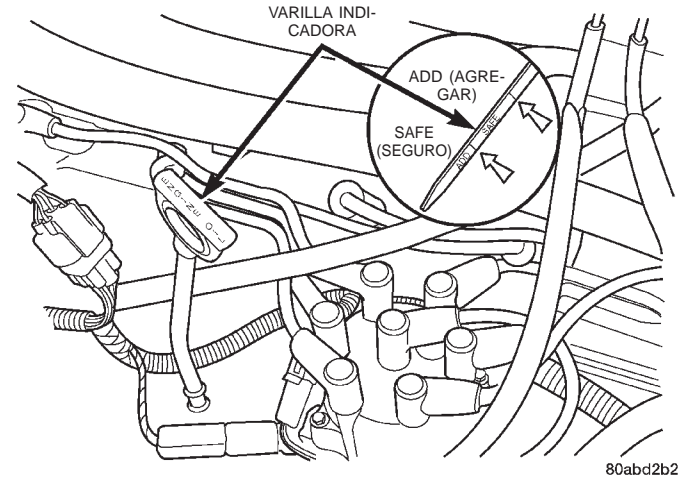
Varilla indicadora de aceite del motor—motor 4.0L
